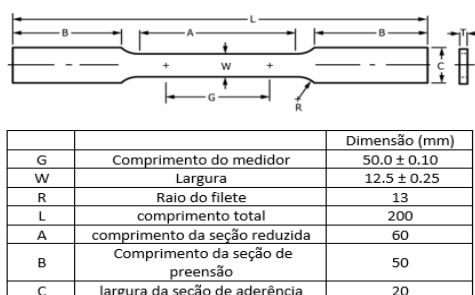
Dimensões da gravata para o ensaio de tração. (ASTM E646)
